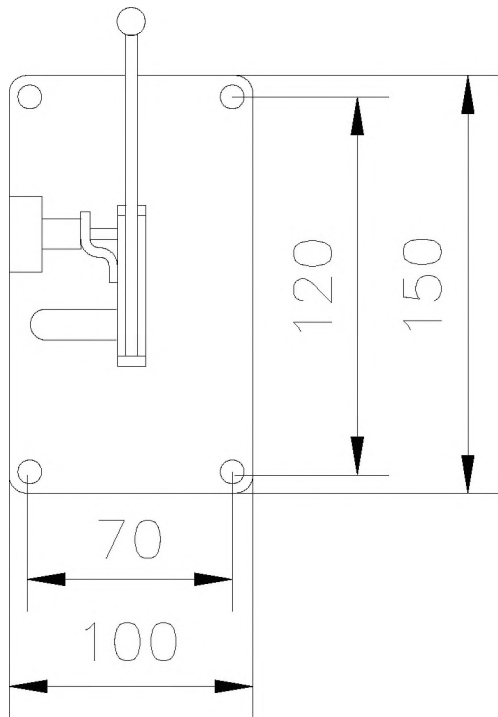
Общий вид, габаритные и установочные размеры разъединителя РРЗ-10/630УЗ с двумя заземляющими ножами
